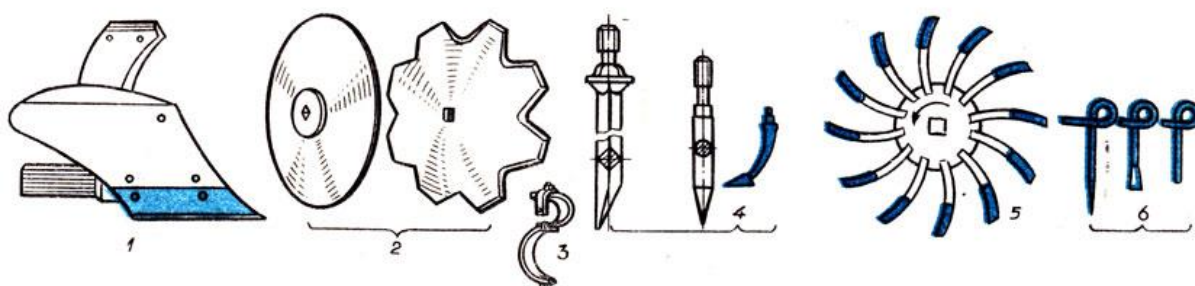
Рабочие органы луцильников и борон: 1 - корпус плуга-луцильника; 2 - сферический и вырезной диски борон и луцильников; 3 - пружинный зуб бороны; 4 - квадратный, круглый и лапчатый зубья бороны; 5 - игольчатый диск бороны; 6 - зубья сетчатой бороны
